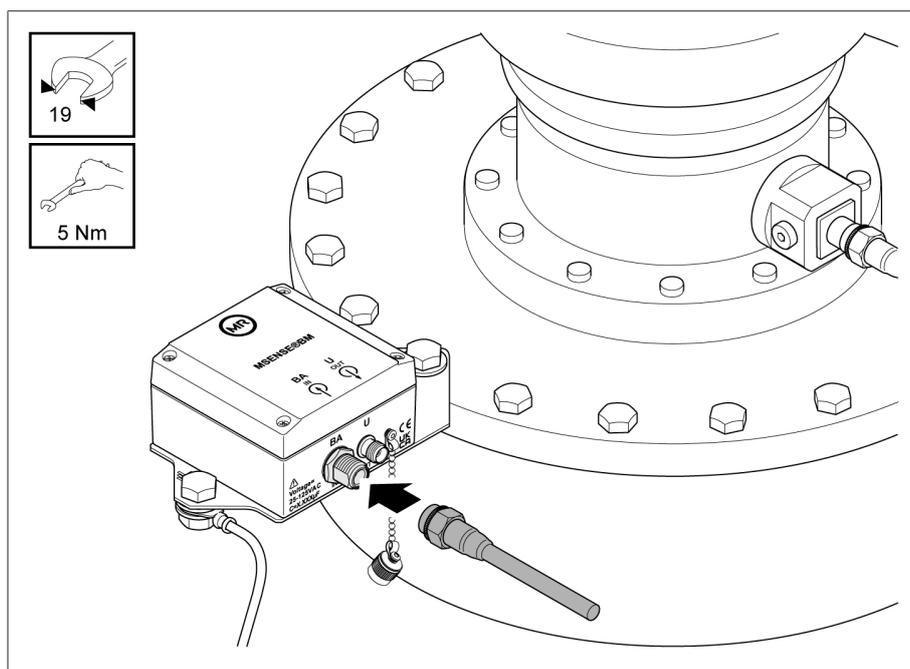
collegamento del cavo di collegamento all'unità di accoppiamento
